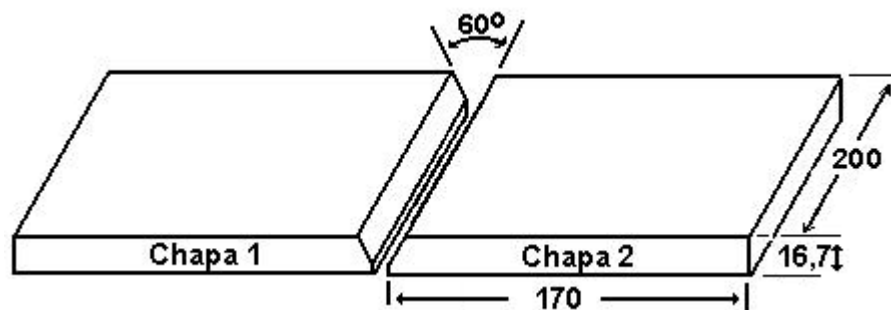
Dimensões das chapas a serem soldadas.
